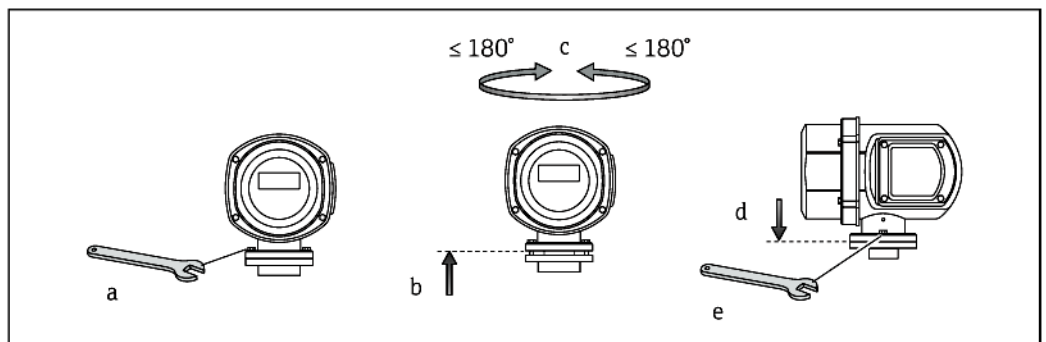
Вращение корпуса трансмиттера (полевой корпус из нержавеющей стали)
